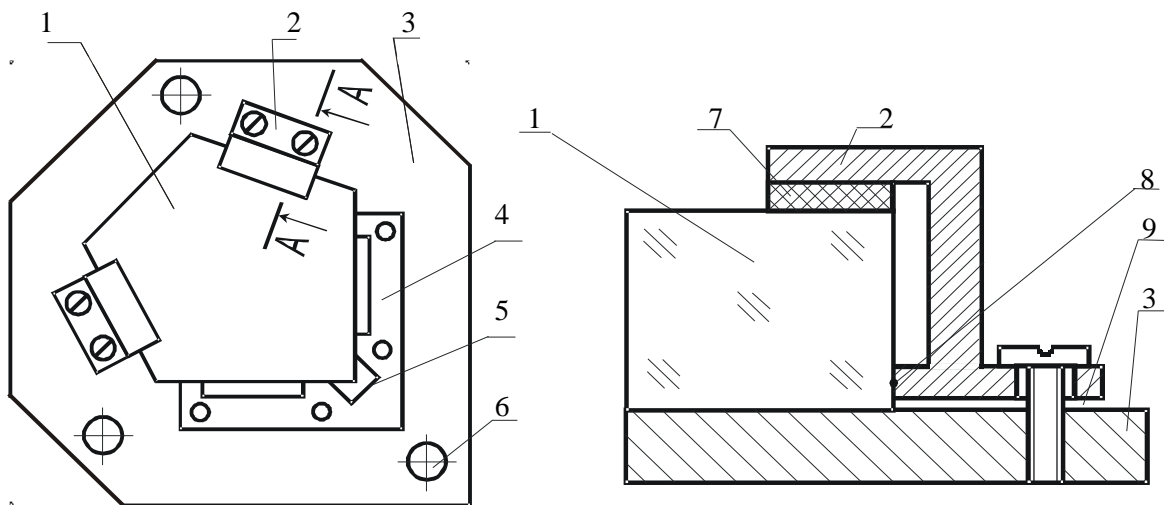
Кріплення кронштейнами: 1 – призма БР-90⁰; 2 – кронштейн; 3 – плато; 4 – установочна планка; 5 – паз, що охороняє ребро призми; 6 – отвір для кріплення призми; 7 – прокладка; 8 – установочний виступ; 9 – зазор, що гарантує притиск призми
